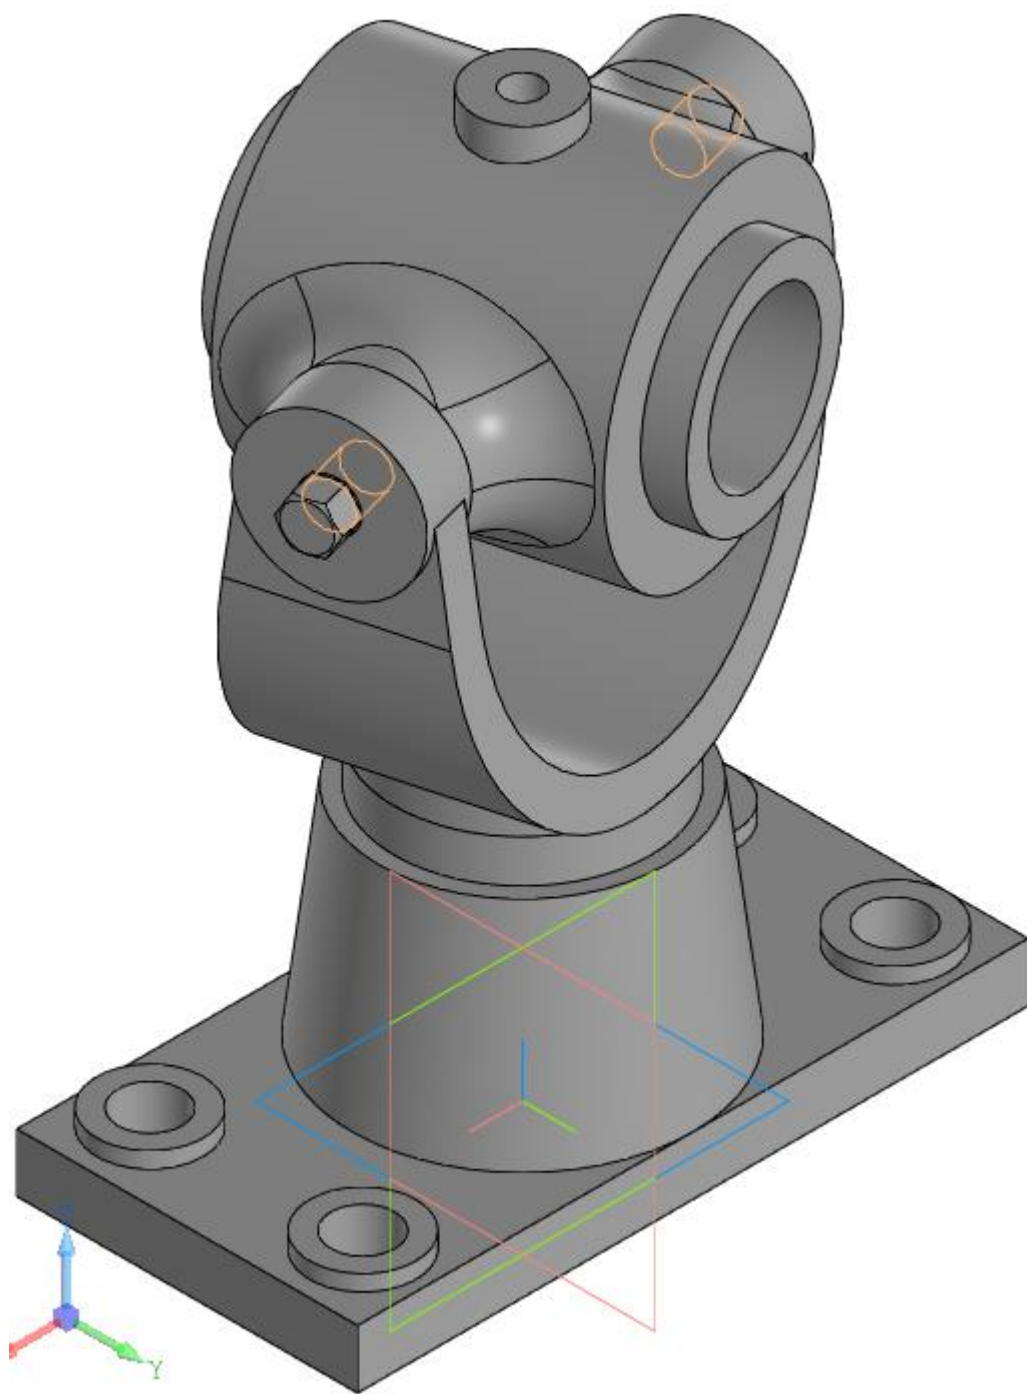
Трехмерная модель сборочной детали, изометрический вид
